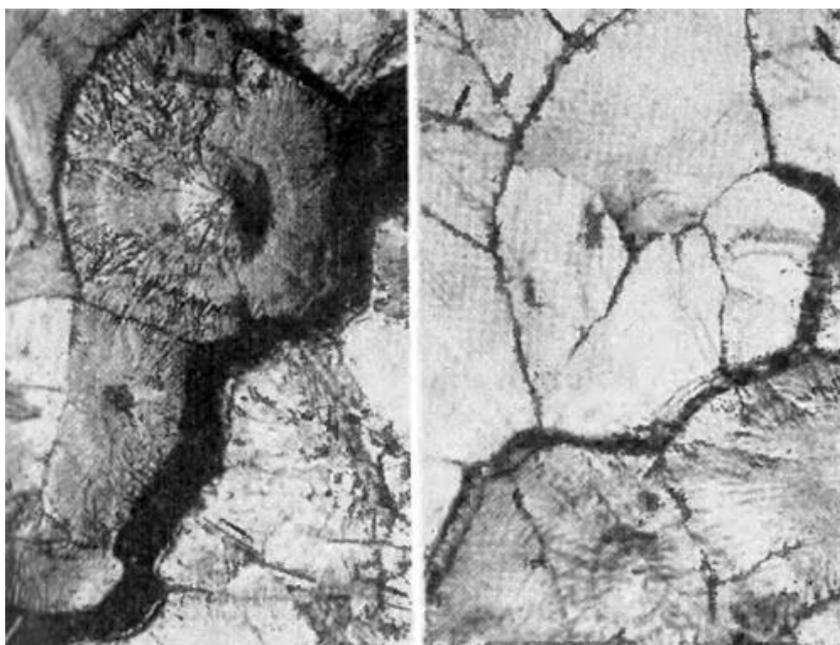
Горячие трещины в металле сварного шва (снимки с поверхности),  $\times 100$
